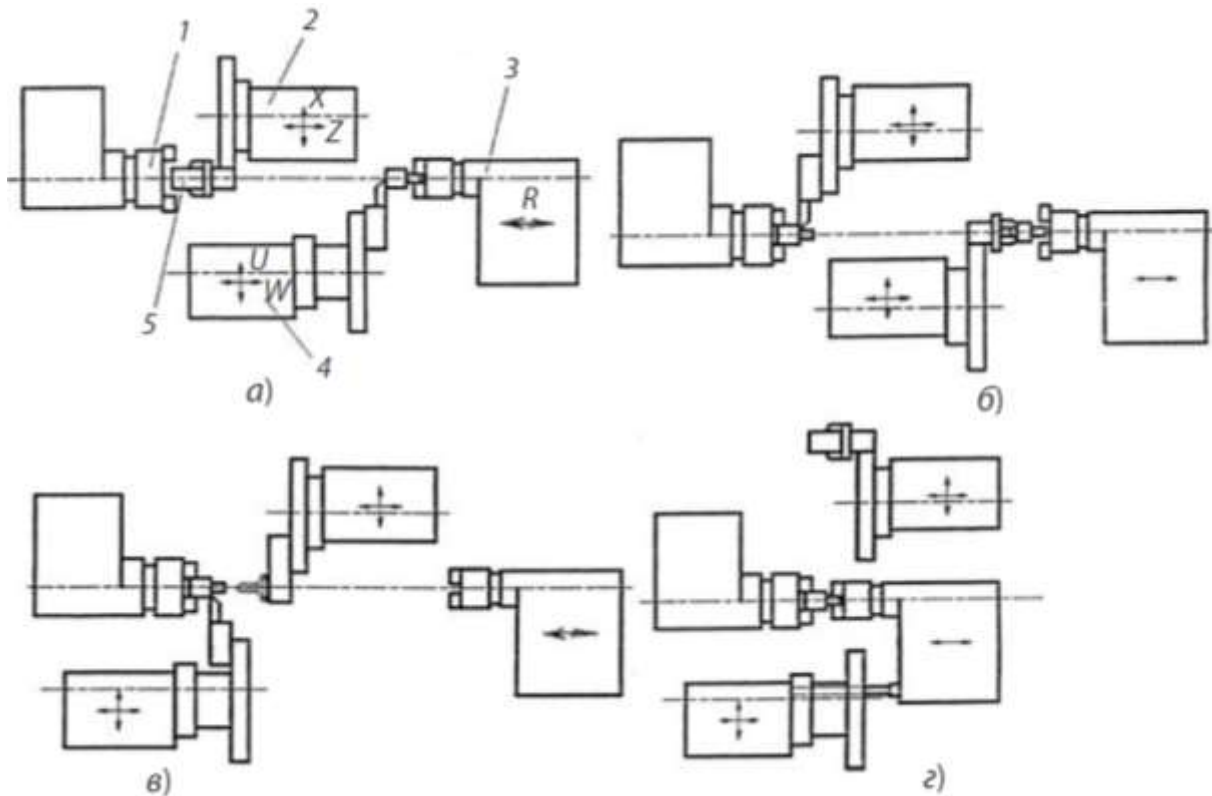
Послідовність обробки заготовки на верстаті з двома револьверними головками і протишпинделем: а – установка заготовки в шпиндель верстата; б – обточування заготовки з револьверної головки 2; в – підрізування з револьверної головки 4; г – перехоплення заготовки в протишпиндель 3 [1].
